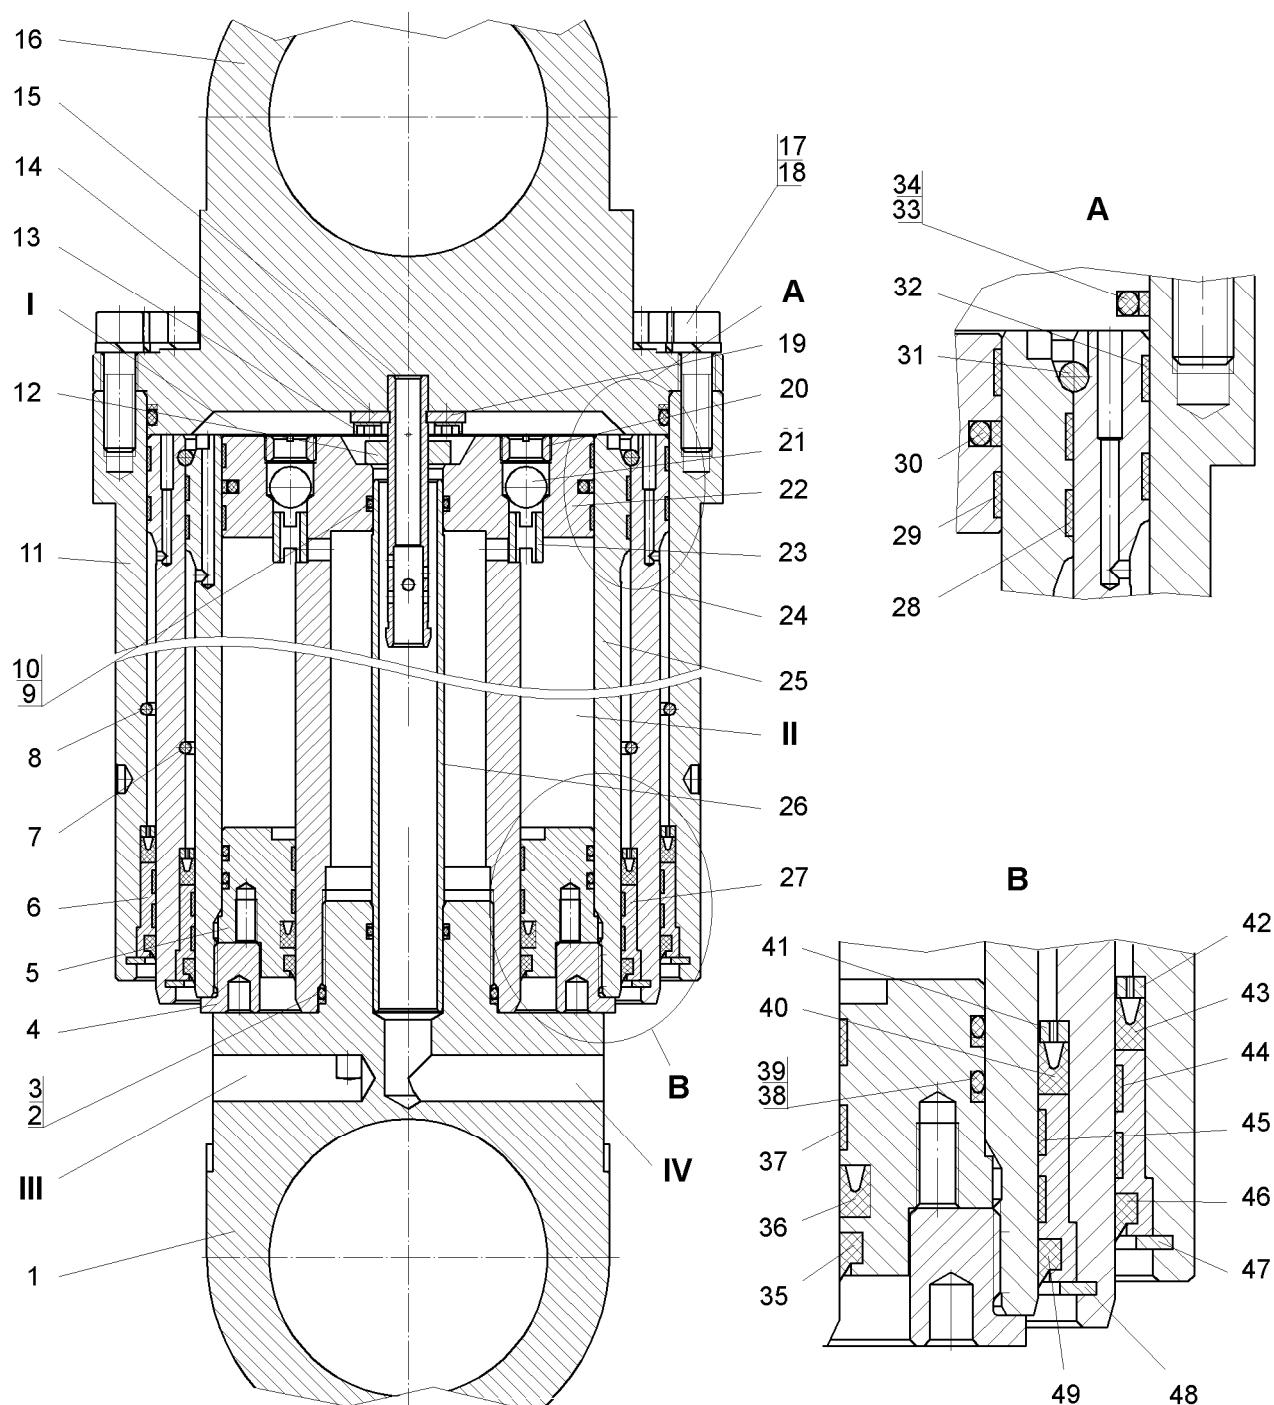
Цилиндр опрокидывающего механизма:
